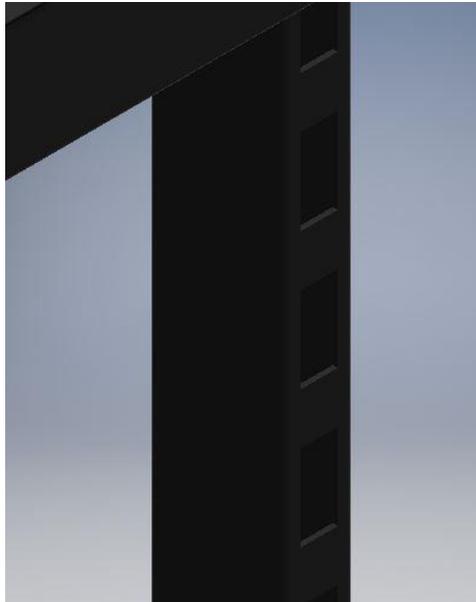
Cremallera de la estructura metálica del Pop Up
